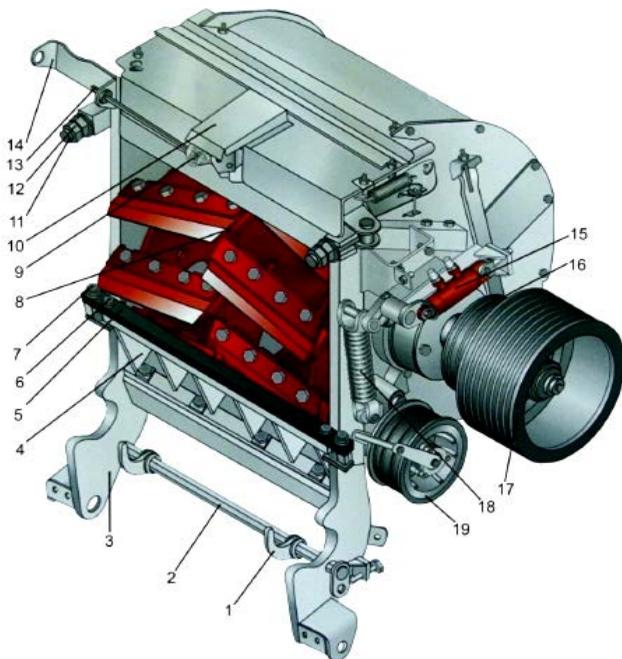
Измельчающий аппарат: 1 – крюк навески питателя; 2 – рычаг навески; 3 – каркас измельчающего барабана; 4 – опора противорежущего бруса; 5 – брус противорежущий; 6 – болт крепления бруса; 7 – эксцентрик регулировки бруса; 8 – измельчающий барабан; 9 – конические шестерни подъема-опускания заточного бруса; 10 – крышка заточного устройства; 11 – стяжка крепления питателя; 12 – гайка стяжки; 13 – ось квадратная заточного устройства; 14 – кронштейн установки ключа; 15 – гидроцилиндр леникса питателя; 16 – шкив привода питателя; 17 – шкив привода измельчающего барабана; 18 – пружина леникса питателя; 19 – шкив леникса питателя
